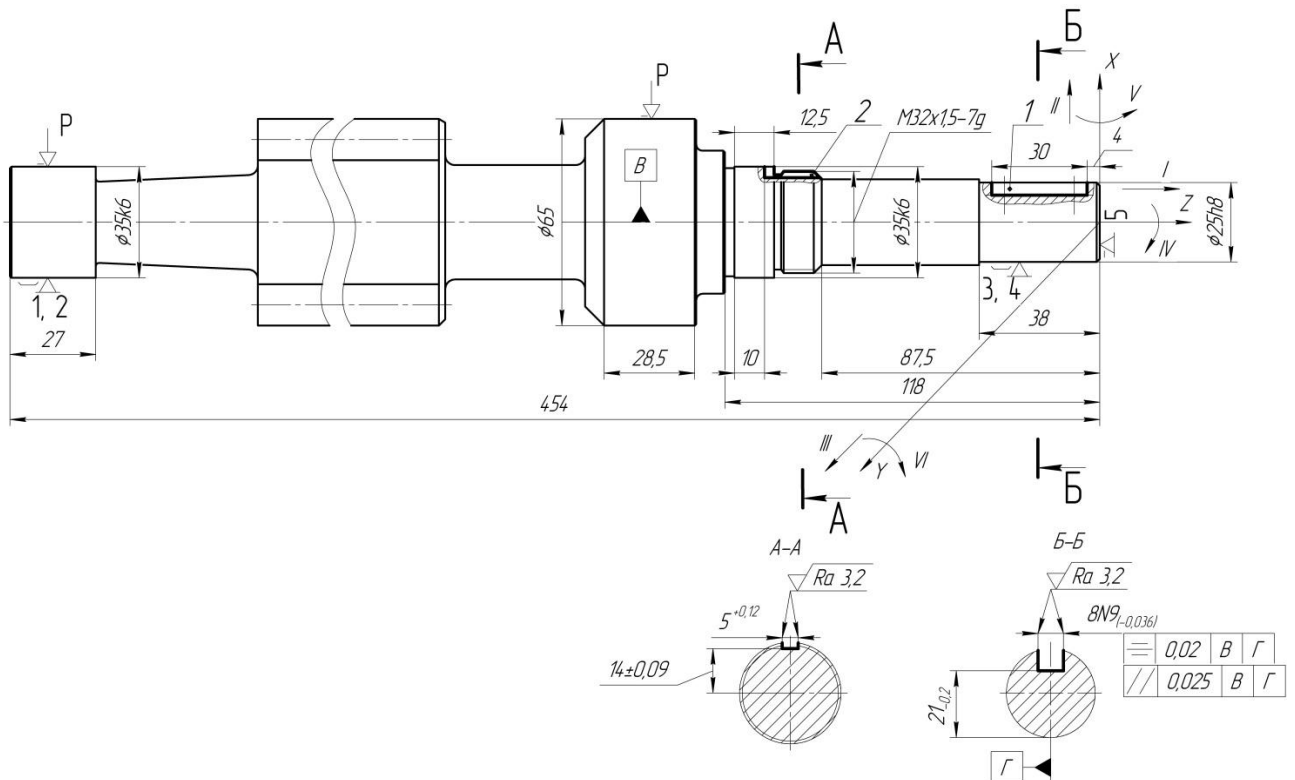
Операционный эскиз операции 030 – фрезерная с ЧПУ. Схема 2.
